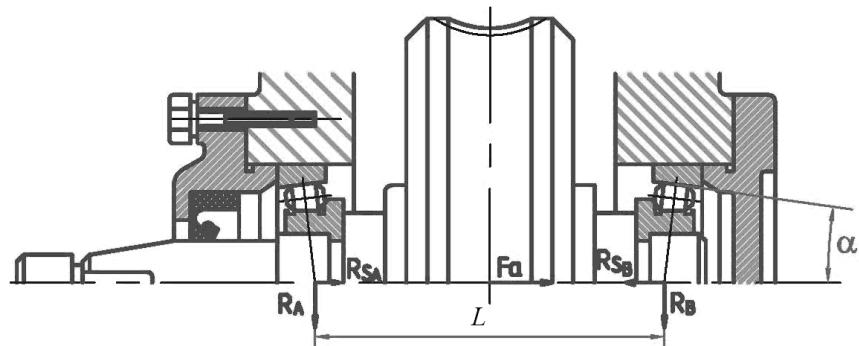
Пример установки вала на роликовых конических подшипниках «враспор»
